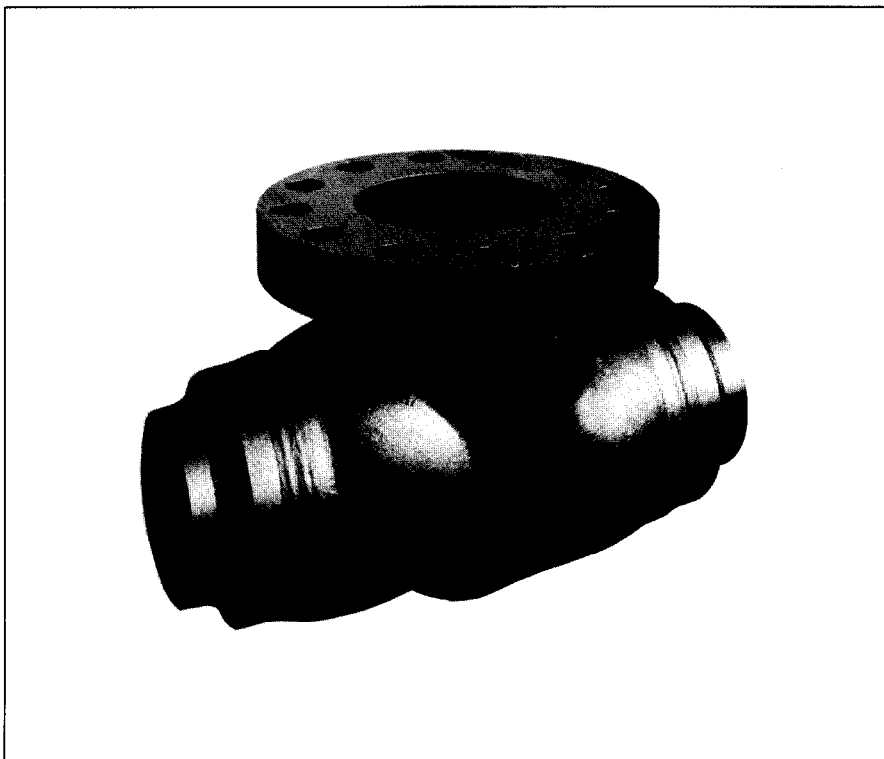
Elektronenstrahlschweißen: Gehäusekörper für Hochdruck-Ventil DN 200, PN 100 (Stückmasse 225 kg, Länge 650 mm) aus 13 CrMo 4.4 V. Schweißquerschnitte: Längsnähte $2 \times 24\,100 \text{ mm}^2$, Sitzringnaht $13\,200 \text{ mm}^2$, Rohrstücknähte $2 \times 20\,100 \text{ mm}^2$, Deckelflanschnaht $31\,400 \text{ mm}^2$
